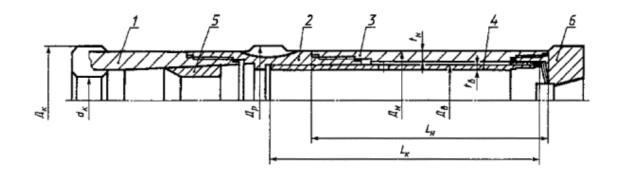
Схема конструкции двойной колонковой трубы типа ТДТ
